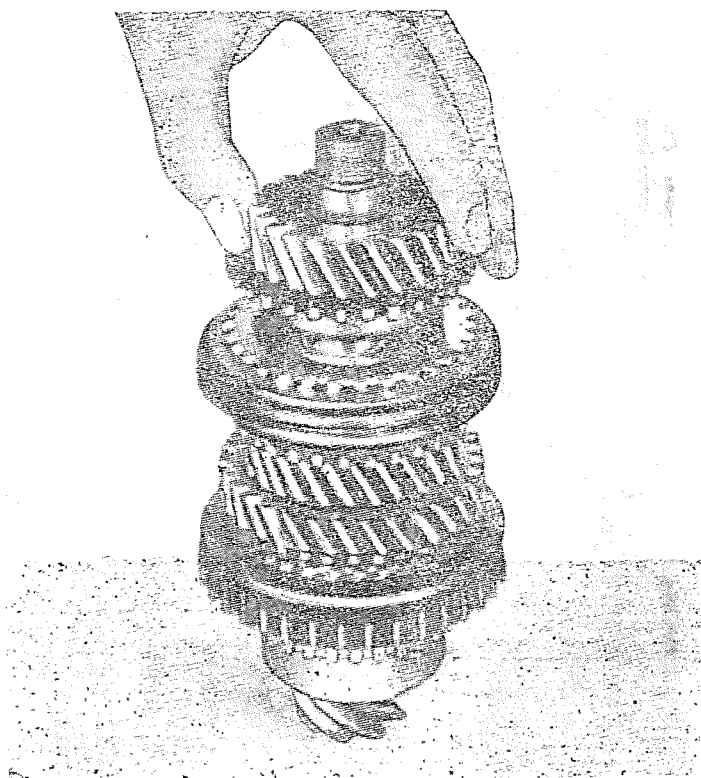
Extracción del engranaje de la 3ª velocidad, junto con el cono sincronizador.
